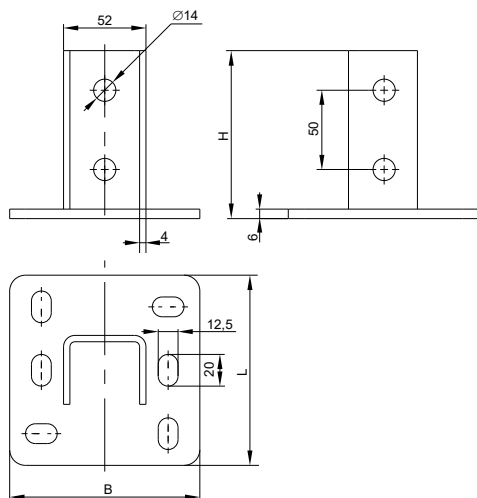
Крепление потолочное для STRUT-профиля / Figure B.1 – Ceiling attachment for STRUT profile
